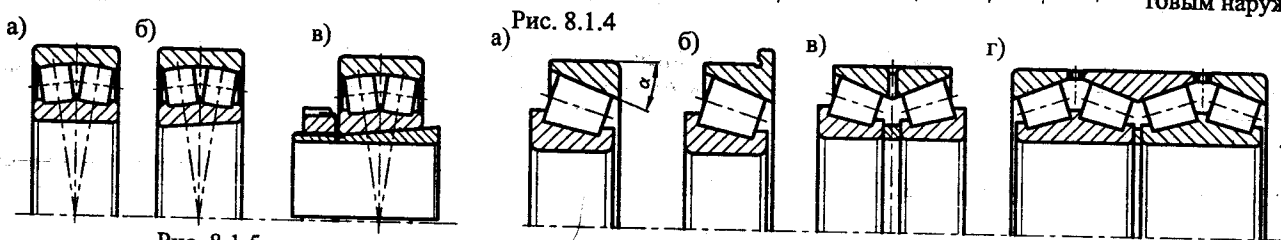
Роликоподшипники радиальные (самоустанавливающиеся):
